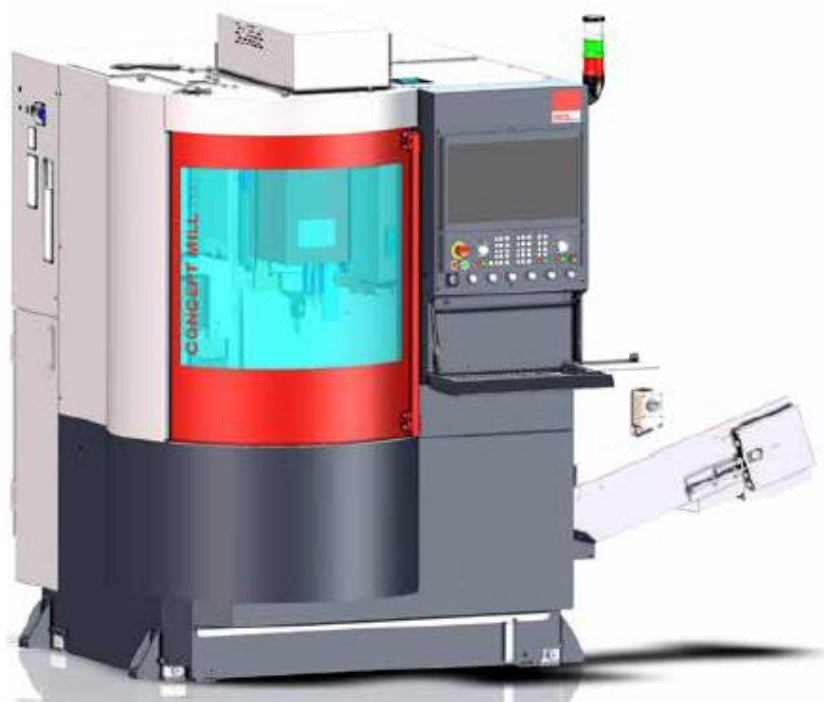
Centro de mecanizado EMCO Concept Mill 260 [32].
